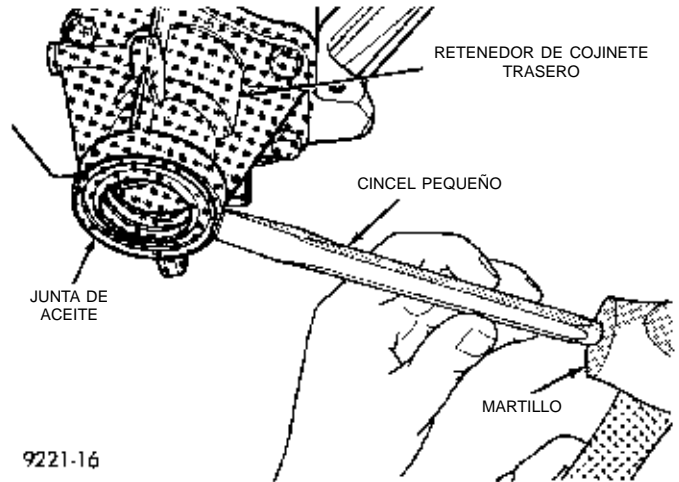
Desmontaje de la junta del retenedor de cojinete trasero
